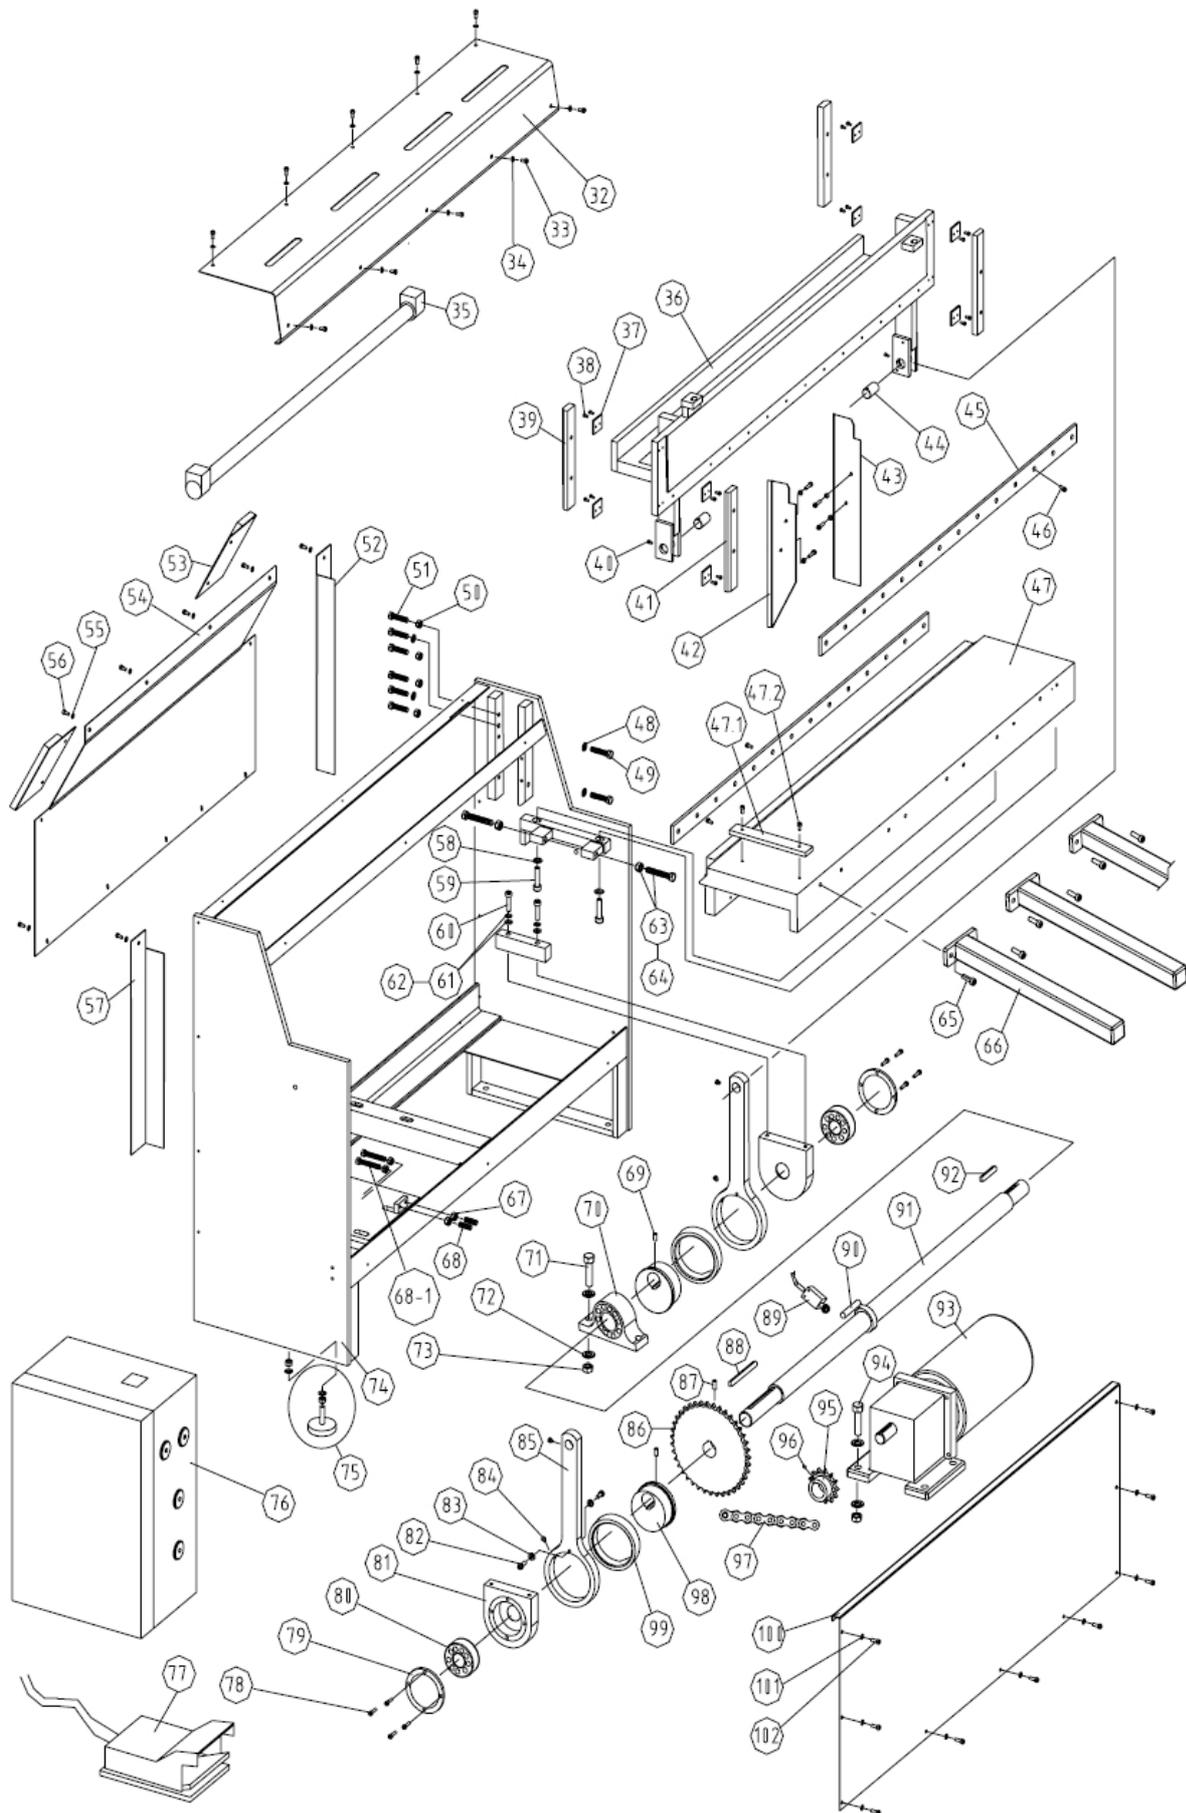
Piezas de dibujo partes de la máquina 2 partes
